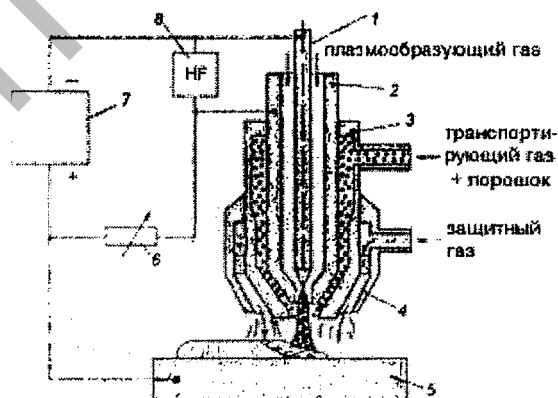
Схема плазменно-порошковой наплавки: 1-электрод;
